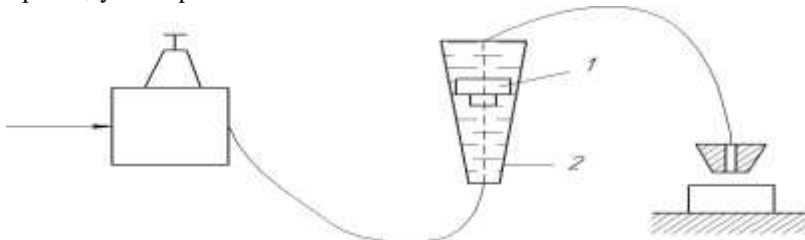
Пневматичні вимірювальні пристрої з ротаметрами
